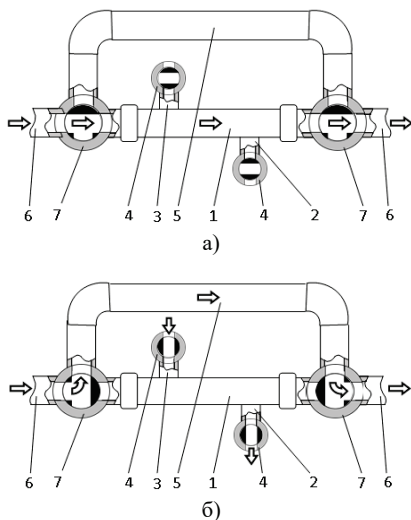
Схематичный чертеж устройства для отбора проб жидкости:
